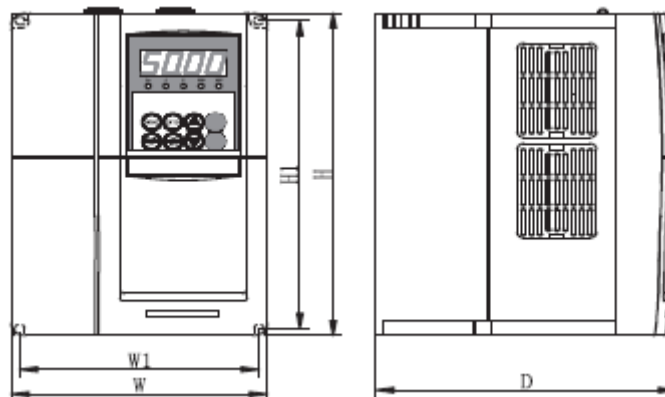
Чертеж с габаритными размерами преобразователя (модель А)
